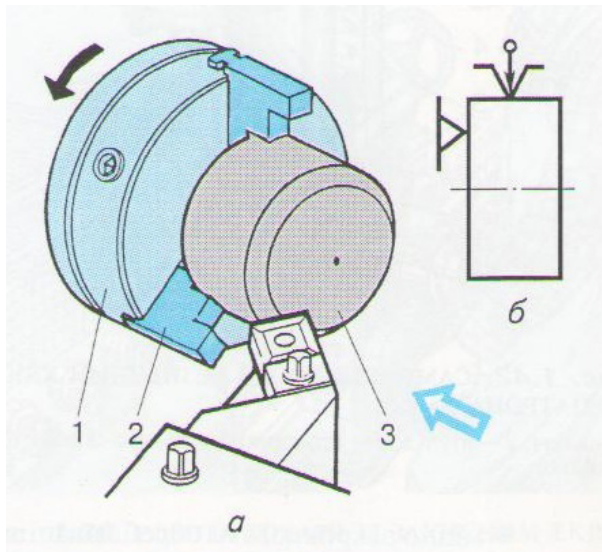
Закріплення заготовки в перевернутих кулачках патрона:
